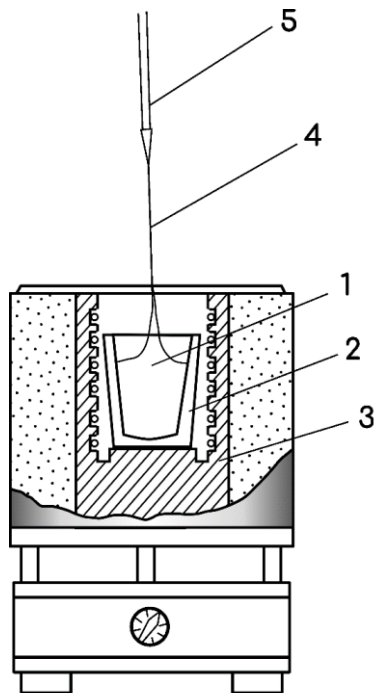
Схема витягування нитки з розплаву скла
